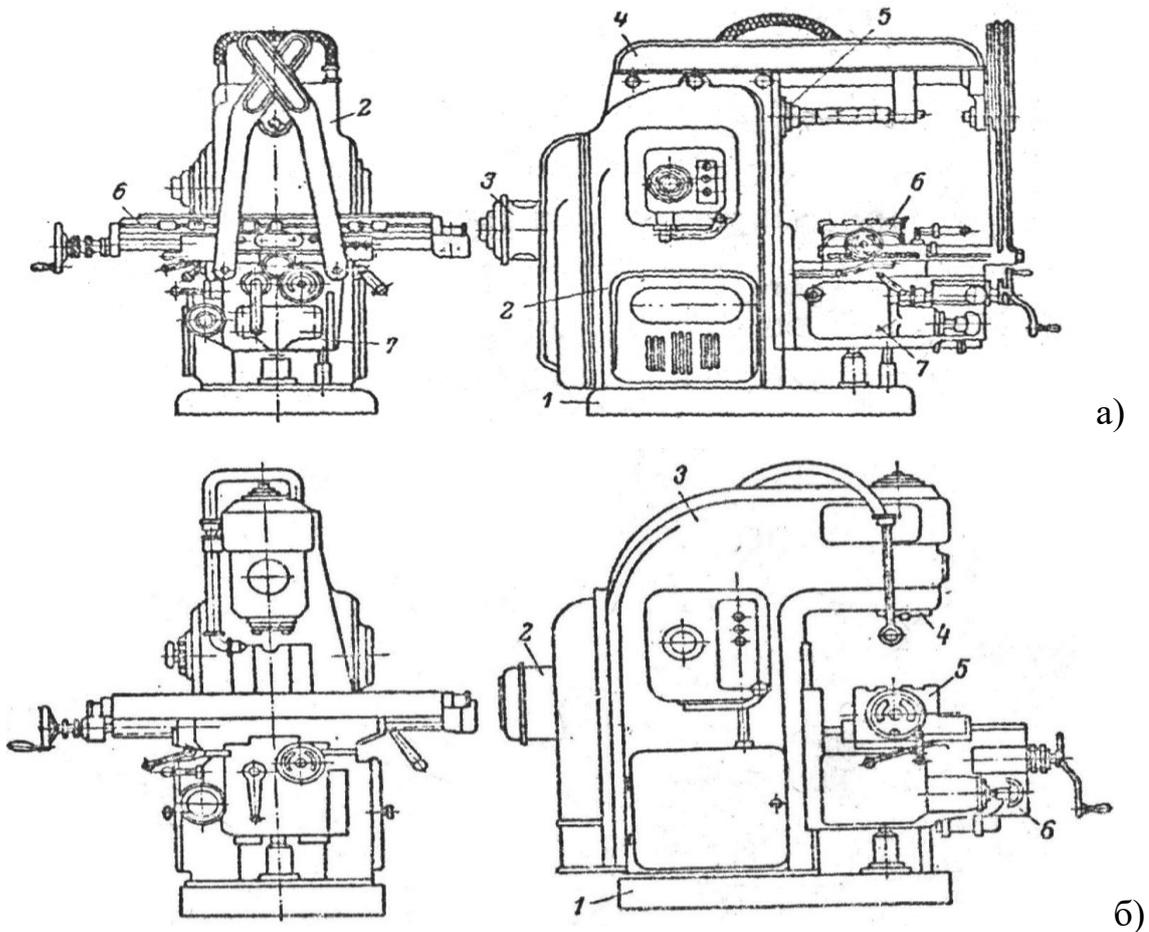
Общий вид универсально фрезерных станков: а – горизонтально-фрезерный; б – вертикально-фрезерный.
